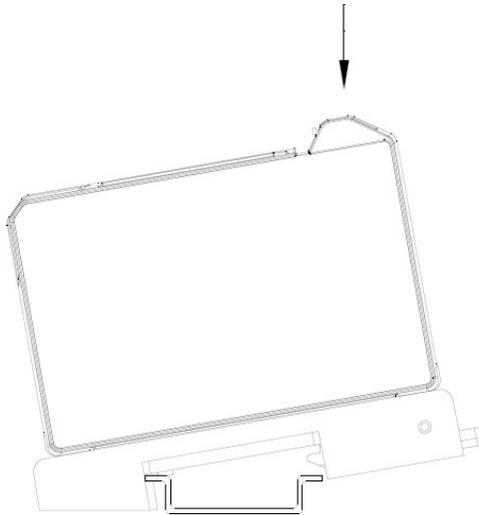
11: Enganche del Sensor en el Carril DIN
